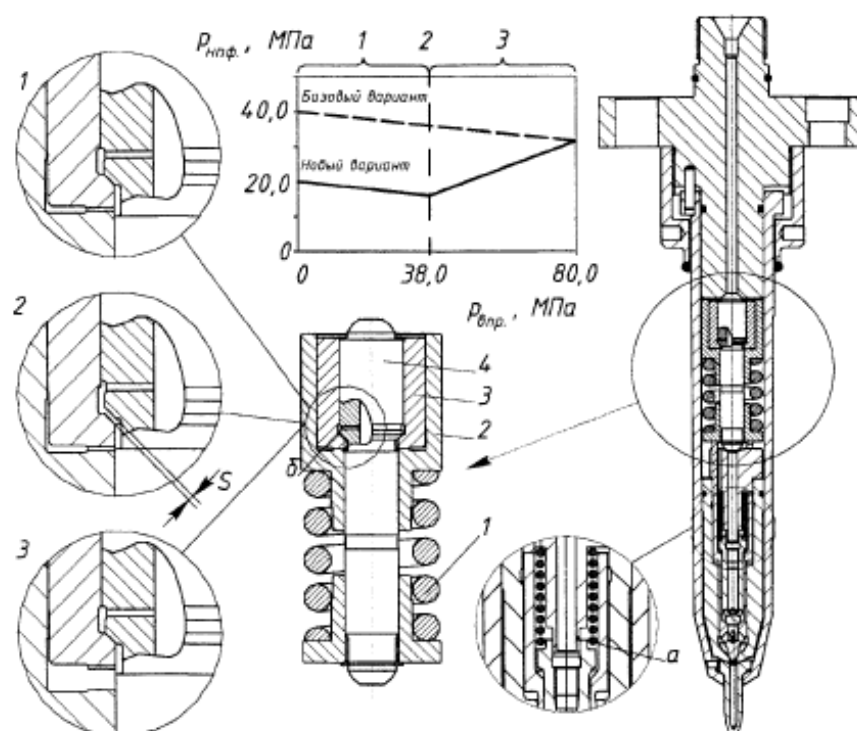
Форсунка малооборотного двигуна з механізмом автоматичної зміни тиску початку уприскування і нижнім розташуванням циркуляційного клапана: *a* – дренажний отвір циркуляційного клапана; *б* – дренажний отвір клапана управління зтягуванням пружини голчастого клапана; *1* – пружина голчастого клапана; *2* – зовнішній поршень; *3* – проміжний поршень; *4* – канал підведення палива до голчастого клапана
